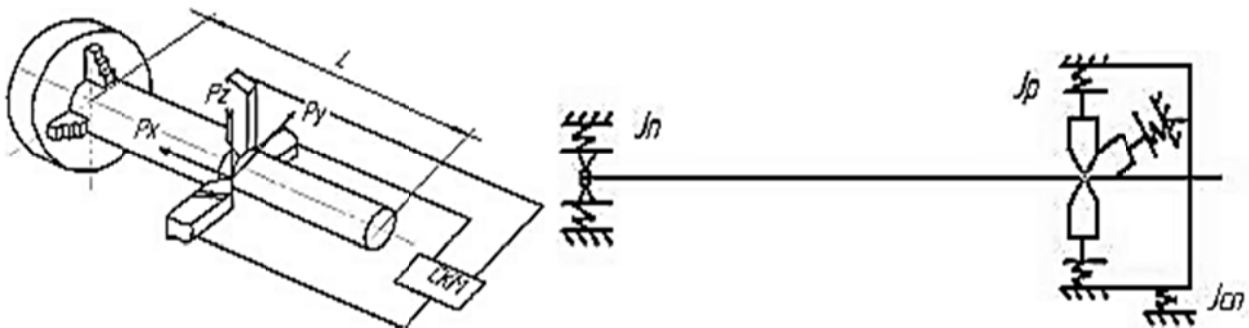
Схема обробки циліндричної деталі трирізцевою головкою
